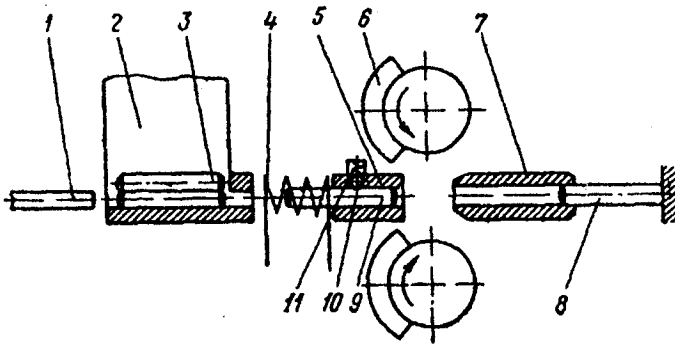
Схема поздовжньо-гвинтової прокатки свердел
